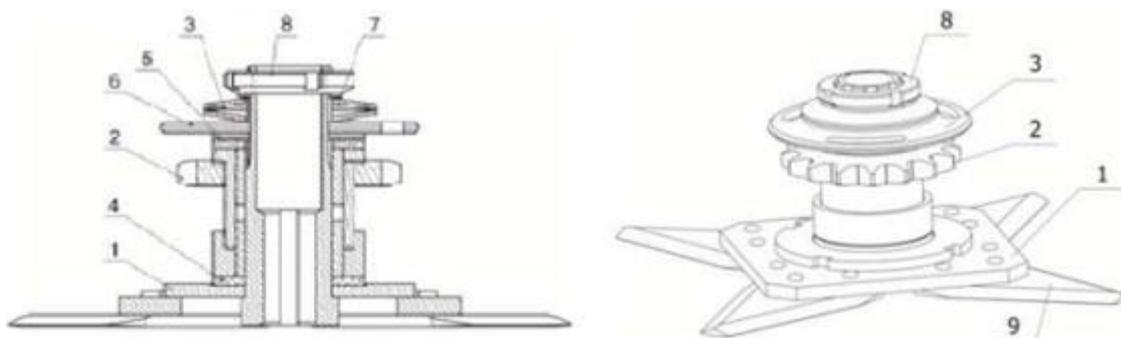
Режущий аппарат ПСП-670:1-диск; 2-звездочка; 3- тарельчатая пружина; 4- фрикционная накладка; 5,6,7-шайба; 8-гайка;9-нож.
